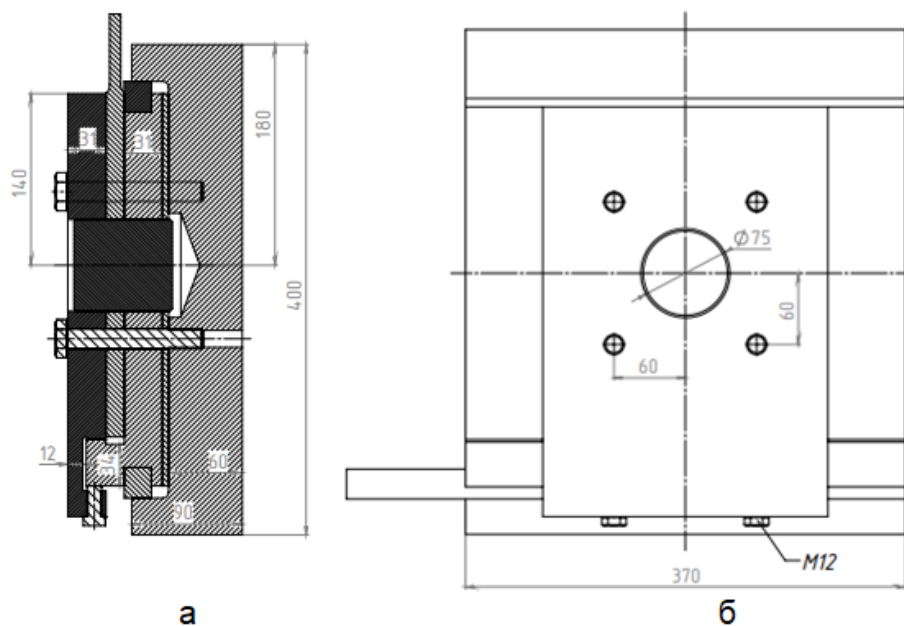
Ескіз вузла кріплення пружини до корпусу статора (а, б)
